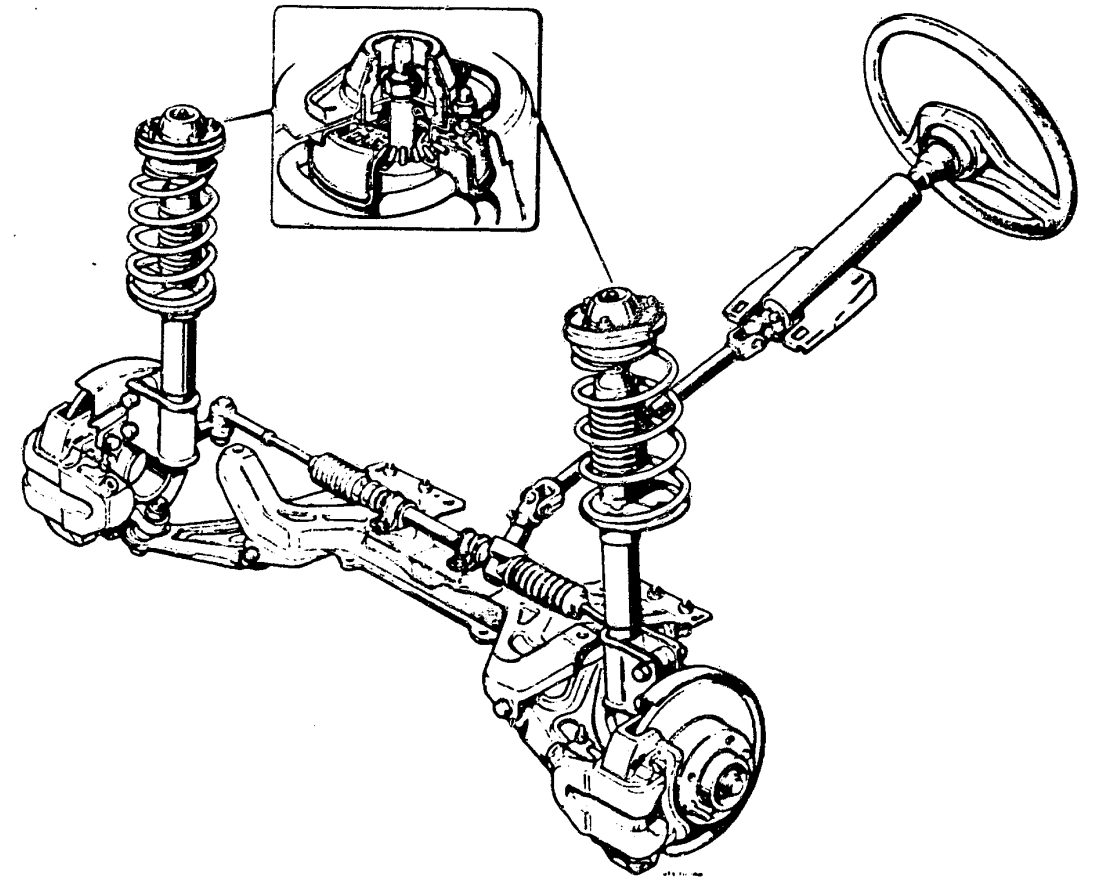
Die Federbein-Vorderradaufhängung mit unteren Dreieckquerlenkern, desaxiierten Schraubenfedern und Zahnstangenlenkung. Oben: Detailzeichnung des Federbeindrehlagers.
